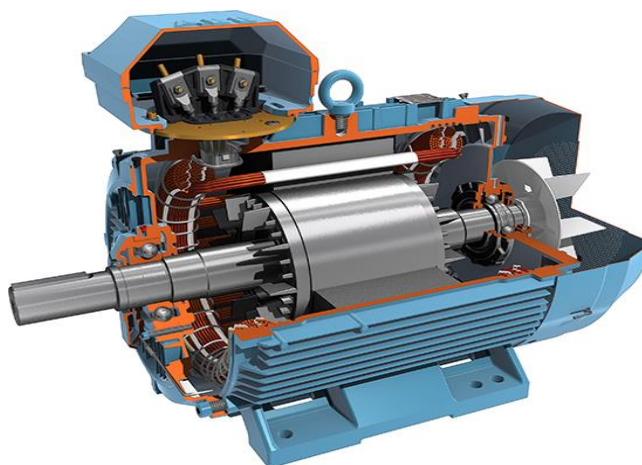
Синхронный двигатель с постоянными магнитами
